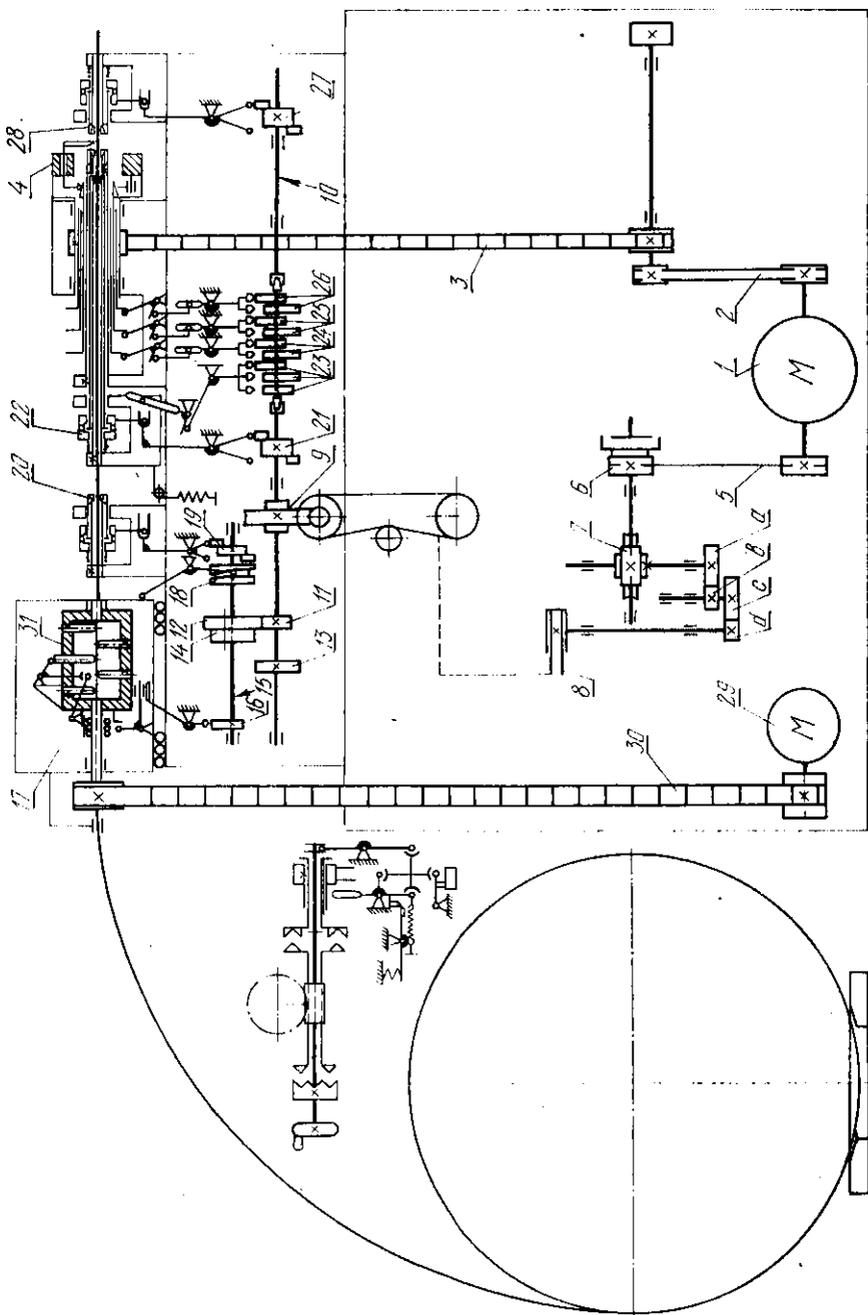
Кинематическая схема двигателя с вращающимся валом
